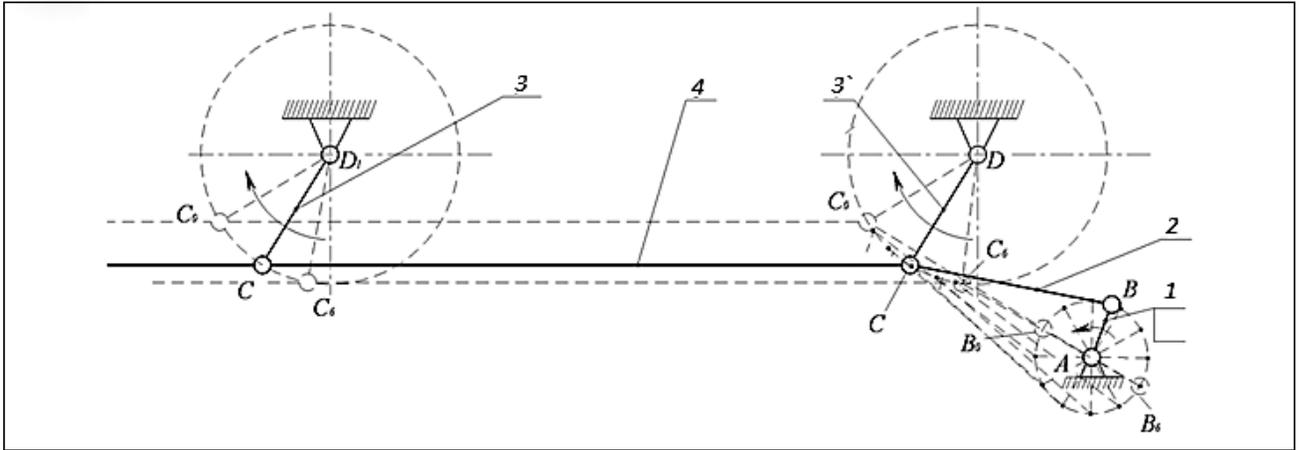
Механизм передачи движения на грохот сортировочной машины: 1 – кривошип; 2 – шатун; 3, 3' – коромысло; 4 – грохот;
